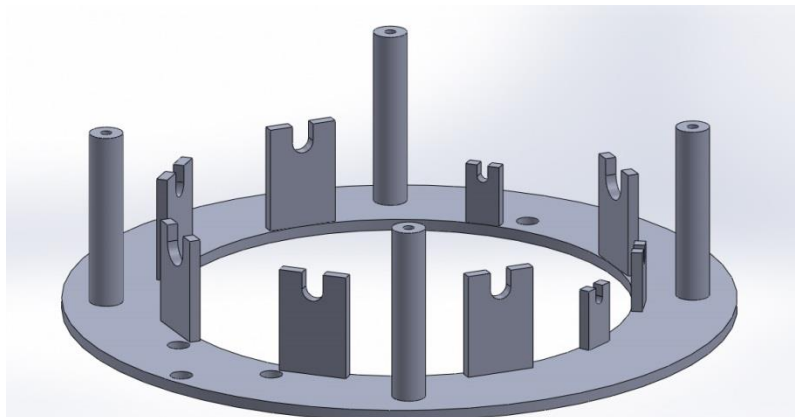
Vista dimétrica del ensamblaje de los pernos.
